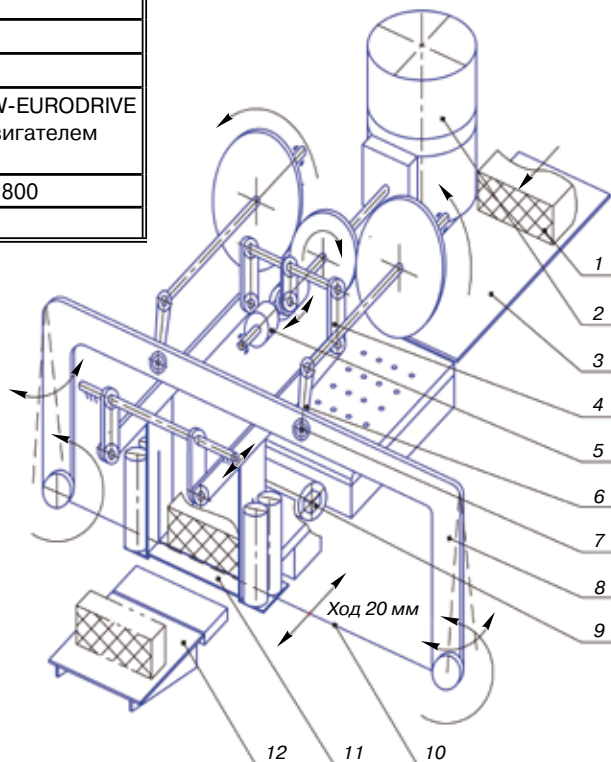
Кинематическая схема автомата РАШЛ-3: 1 – пластичный брус; 2 – сервопривод; 3 – склиз входной; 4 – тяга шарнирная; 5 – кулачок приводной; 6 – кривошип; 7 – опора шаровая; 8 – лучок; 9 – датчик скорости перемещения; 10 – струна; 11 – столик подвижный; 12 – склиз выходной
